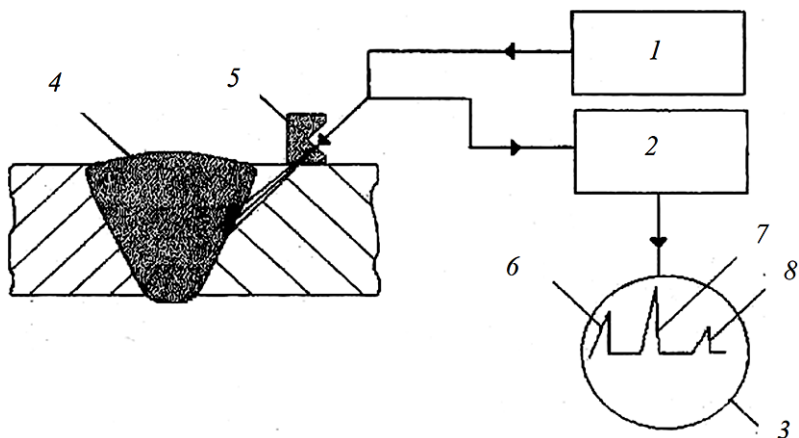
Ультразвуковой контроль сварных соединений:
